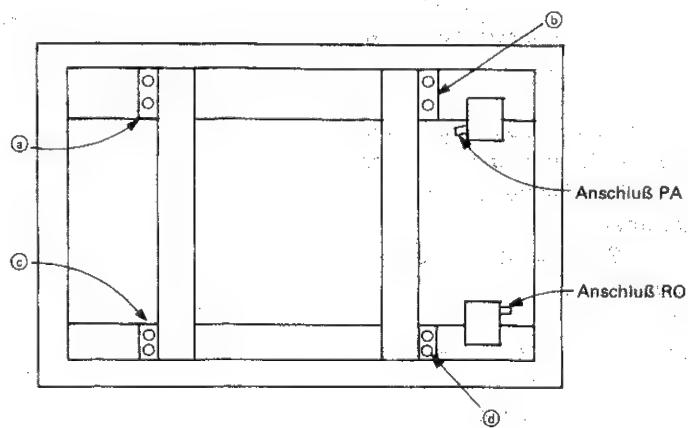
Drehmechanismuseinheit mit entfernter Rückwand
